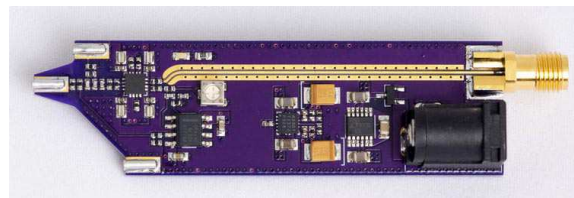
Сборка прототипа активного щупа на четырехслойной печатной плате, изготовленной OSH Park.
